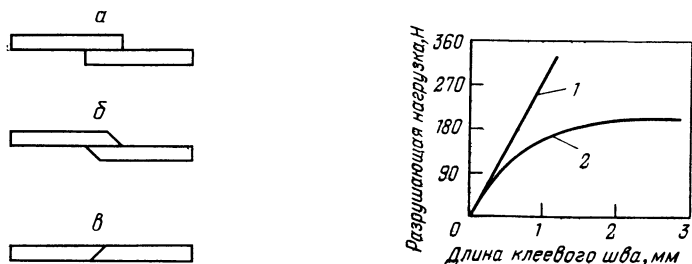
Образцы для испытаний клеевых соединений при статическом сдвиге: *а* — стандартный образец для испытаний на сдвиг; *б* — стандартный образец со снятыми кромками; *в* — соединение на ус.
